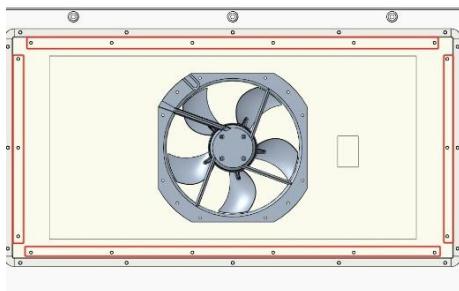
49 Orifícios de fixação da placa de montagem do ventilador de refrigeração
